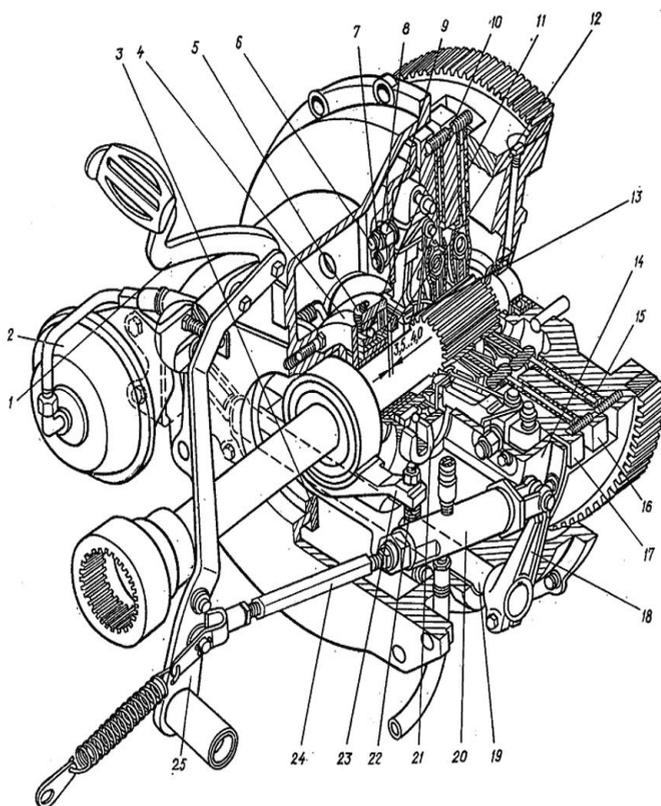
Регулировка сцепления: 1 — педаль; 2 — пневматическая камера; 3 — стакан; 4 — корпус выжимного подшипника; 5 — масленка; 6 — вилка; 7 — болт; 8 — стопорная пластина; 9 — гайка регулировочная; 10 — подшипник выжимной; 11 — упор выжимного подшипника; 12 — кольцо упорное; 13 — отжимной рычаг; 14 — кожух; 15 — диск ведомый; 16 — диск промежуточный; 17 — диск нажимной; 18 — рычаг; 19 — валик выключения; 20 — клапан пневмосервомеханизма; 21 — вилка двойная; 22 — пружина тормозка; 23 — колодка тормозка; 24 — тяга пневмосервомеханизма; 25 — рычаг педали
